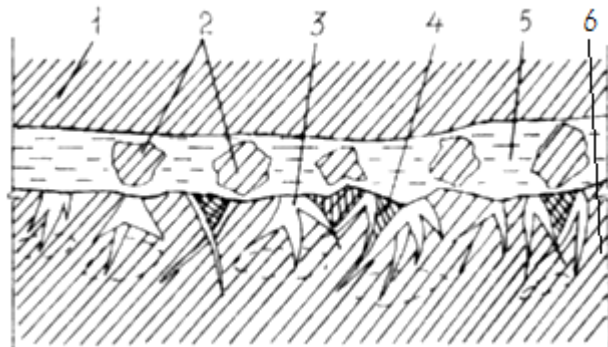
Модель полирования свободным абразивом: 1 –полировальный круг; 2 – зерна абразива; 3 – конические трещины; 4 – выколки; 5 – суспензия; 6 – обрабатываемая поверхность
